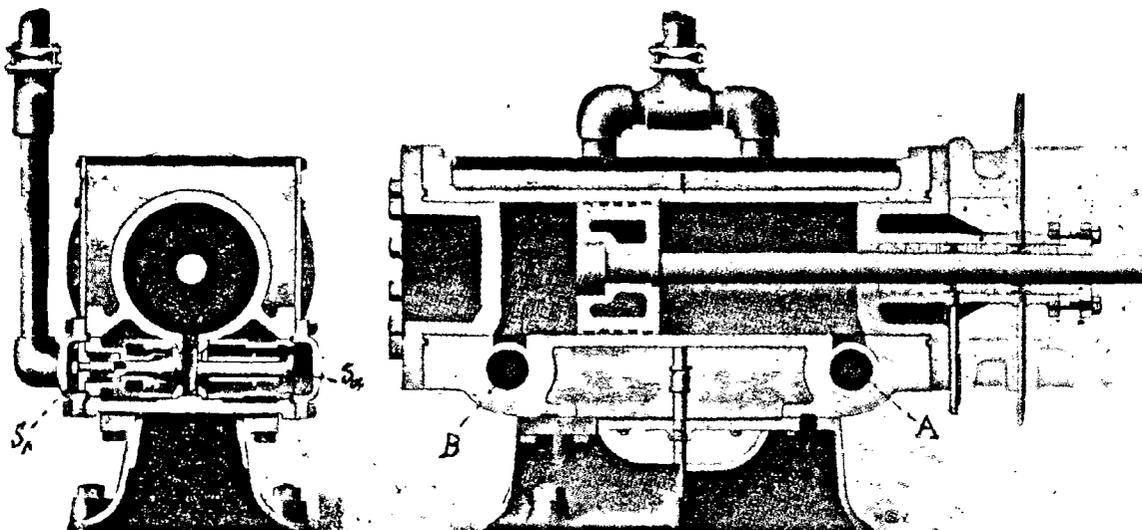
Compresseur horizontal de La Vergne (type 1905).
